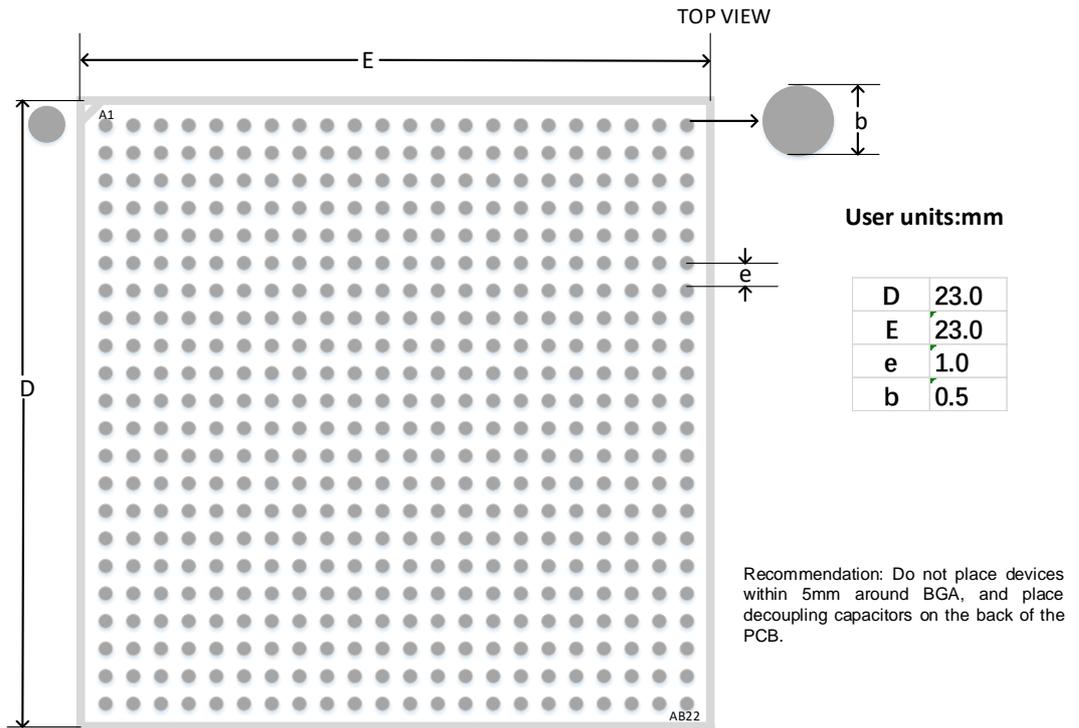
推荐 PCB Layout PG484A (GW5AT-138)
